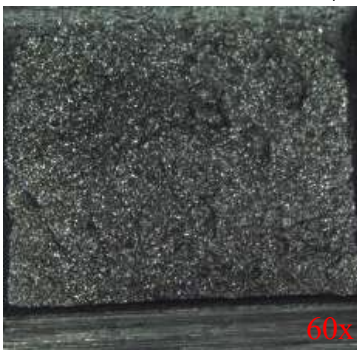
Vista macroscópica de la fractura 22MnB5, -22°C, condición 1.
